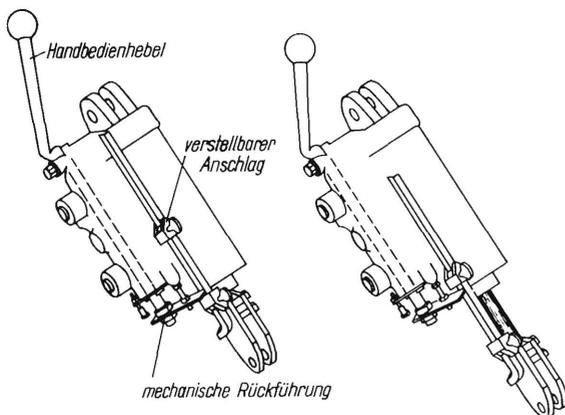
Freier hydraulischer Arbeitszylinder mit mechanischer Rückführung.
